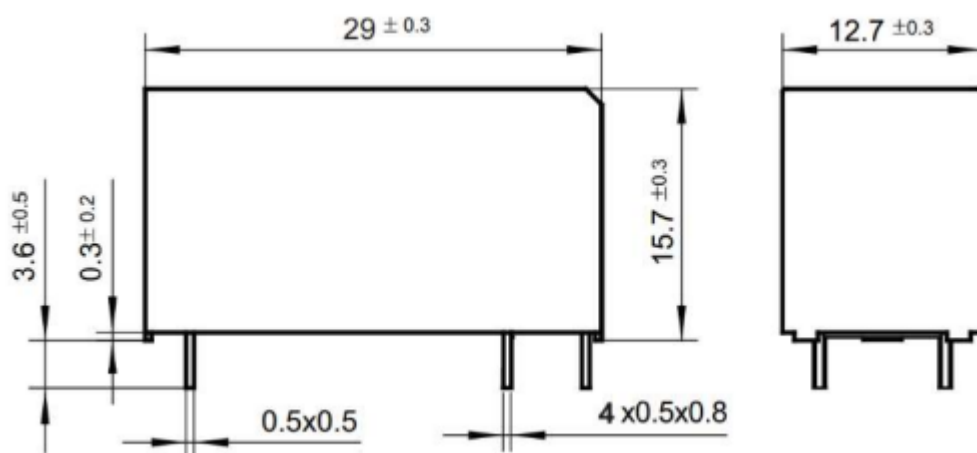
Габаритные, установочные, присоединительные размеры реле
